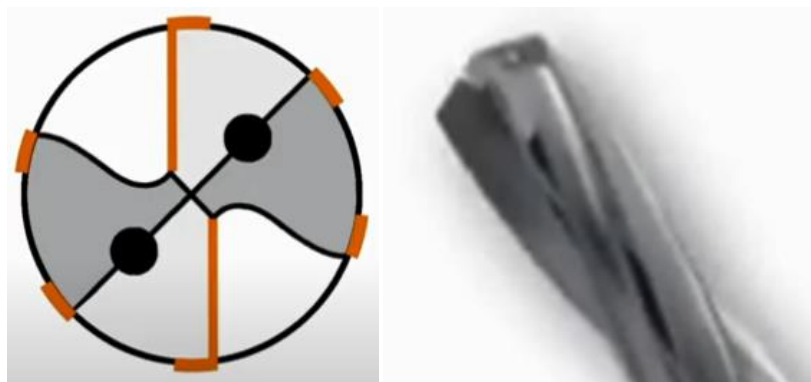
Схема розміщення шести напрямних стрічок та різальна частина свердла
